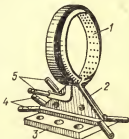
Индуктор для закалки способом одновременного нагрева цилиндрической детали:
